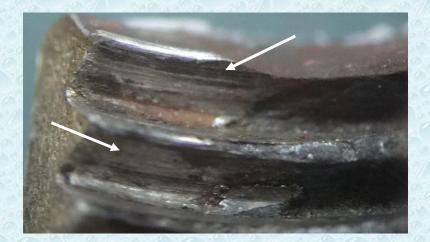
Вид резьбовой части болта. Стрелками показаны: 1 – следы износа на поверхностях вершин витков резьбы; 2 – смятие материала вершин витков.
